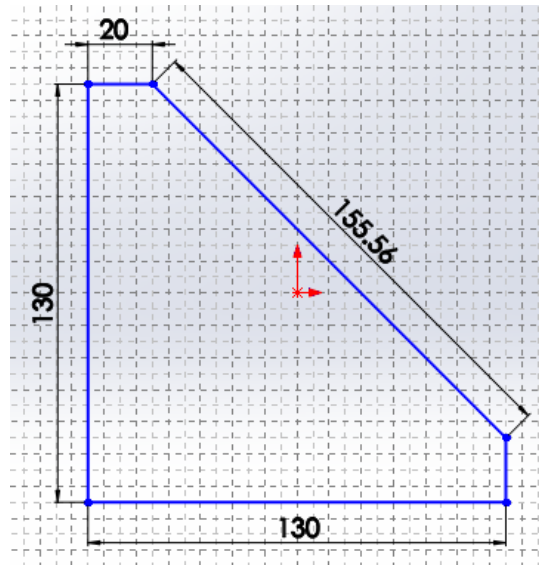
Geometría y dimensiones en cm del panel solar.
